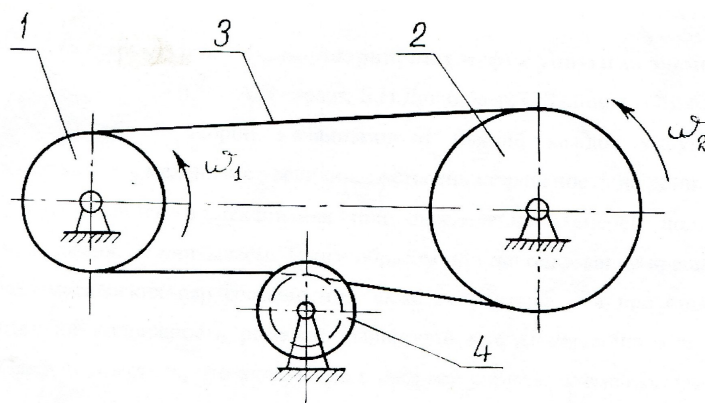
Кинематическая схема плоскоременная передачи с натяжным роликом.
